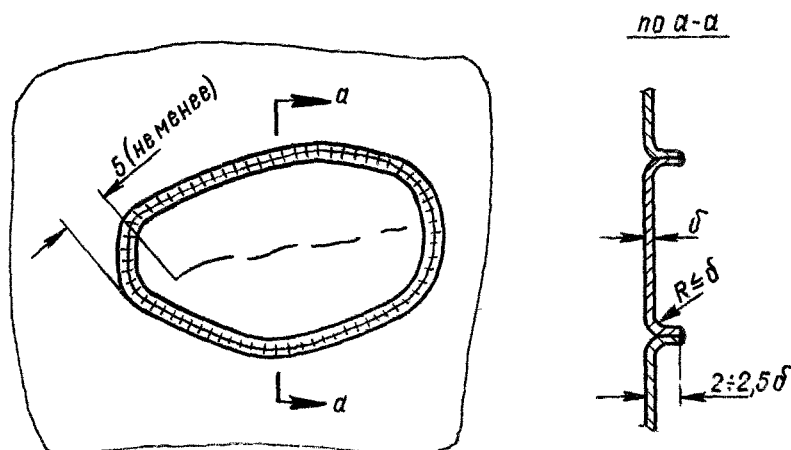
Типовая подготовка под сварку вырезанного дефекта (сварка производится без присадочного материала путем расплавления дугой отбортованных кромок)
